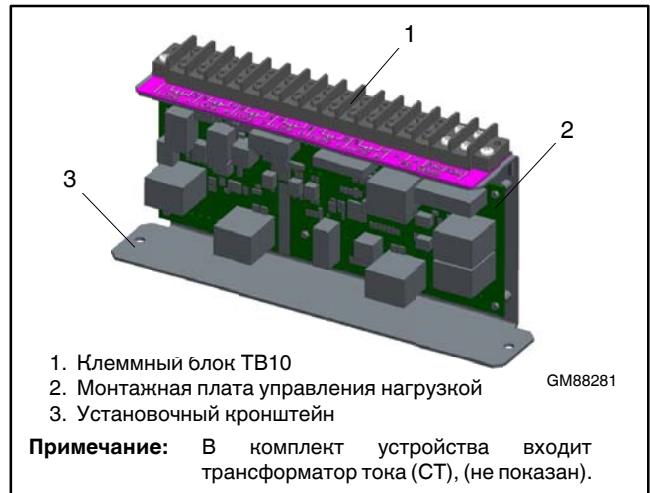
Устройство сброса нагрузки GM88281-1 (устанавливается в корпусе переключателя резерва)
